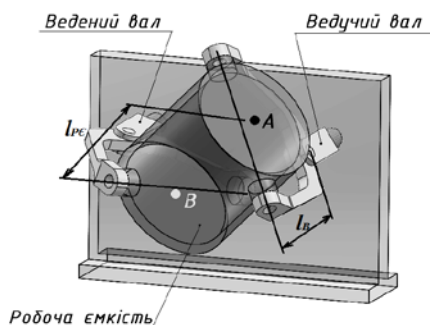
Схема машини для обробки деталей зі складним рухом робочої ємкості
